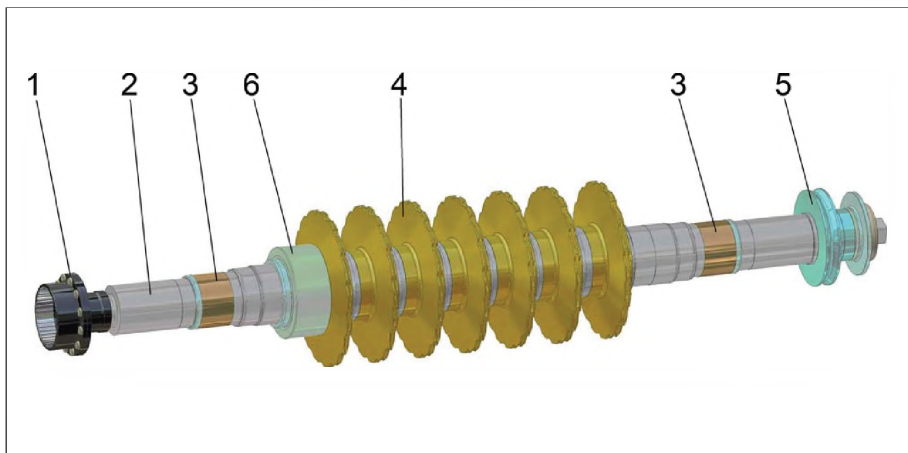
Ротор КВД: 1 – полушар; 2 – вал; 3 – втулки уплотнения; 4 – рабочее колесо; 5 – диск упорный; 6 – думмис
